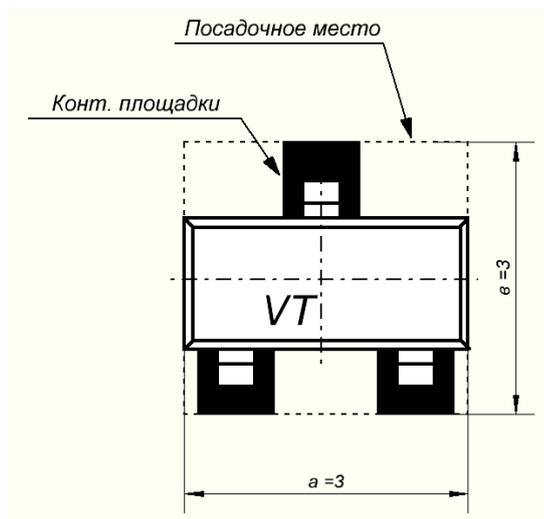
Схема размеров посадочного места для корпуса SOT-23
